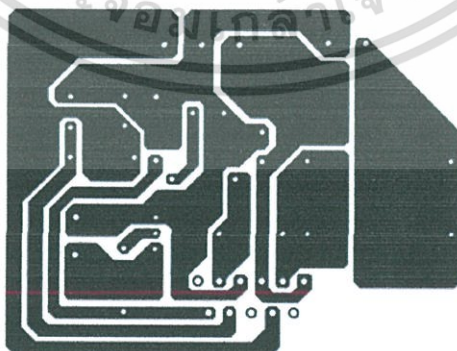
PCB ของแหล่งจ่ายไฟ
